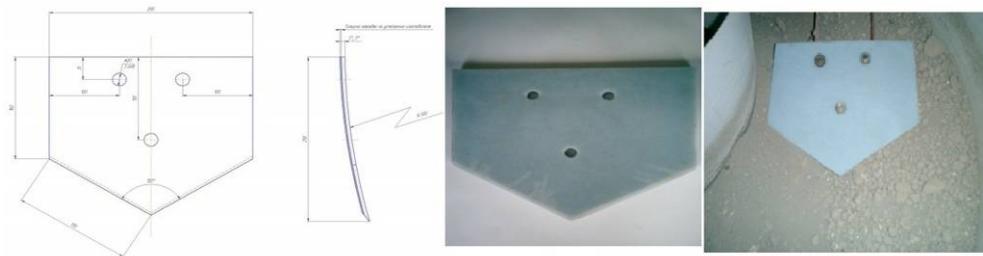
Чертеж, вид и способ установки заданной детали – лопатка.
